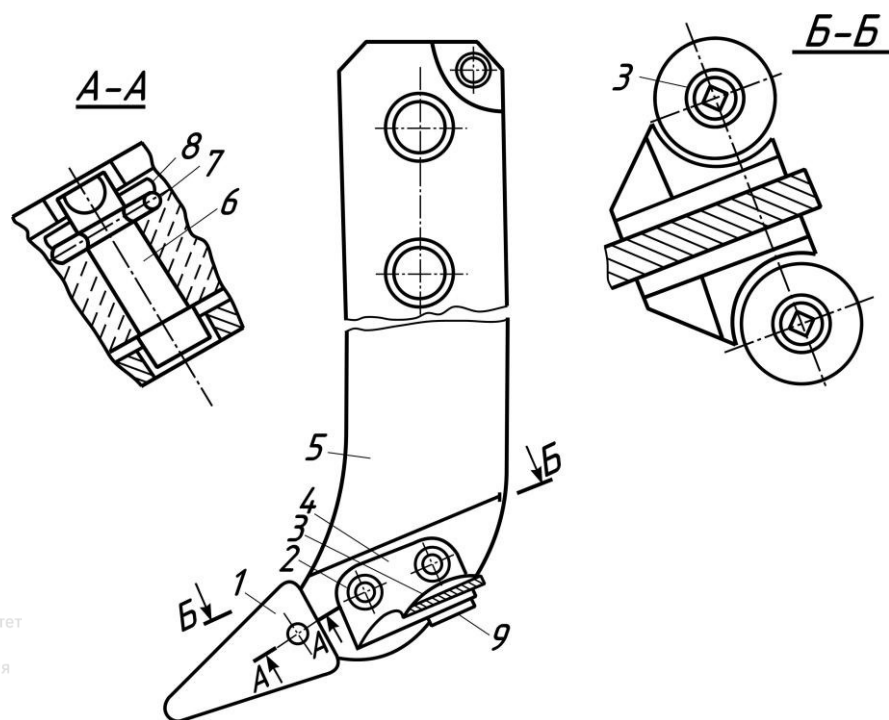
Конструкція зуба розпушувача з розширювачами:
